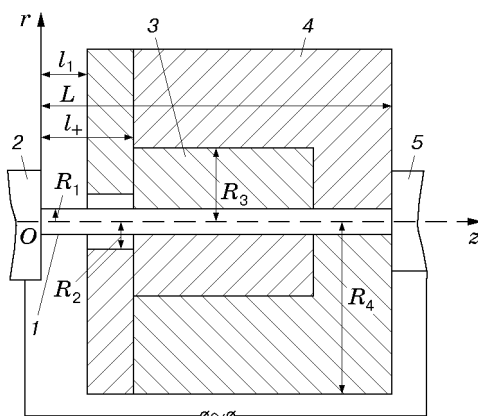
Схема электроконтактного нагрева заготовки для высадки:
